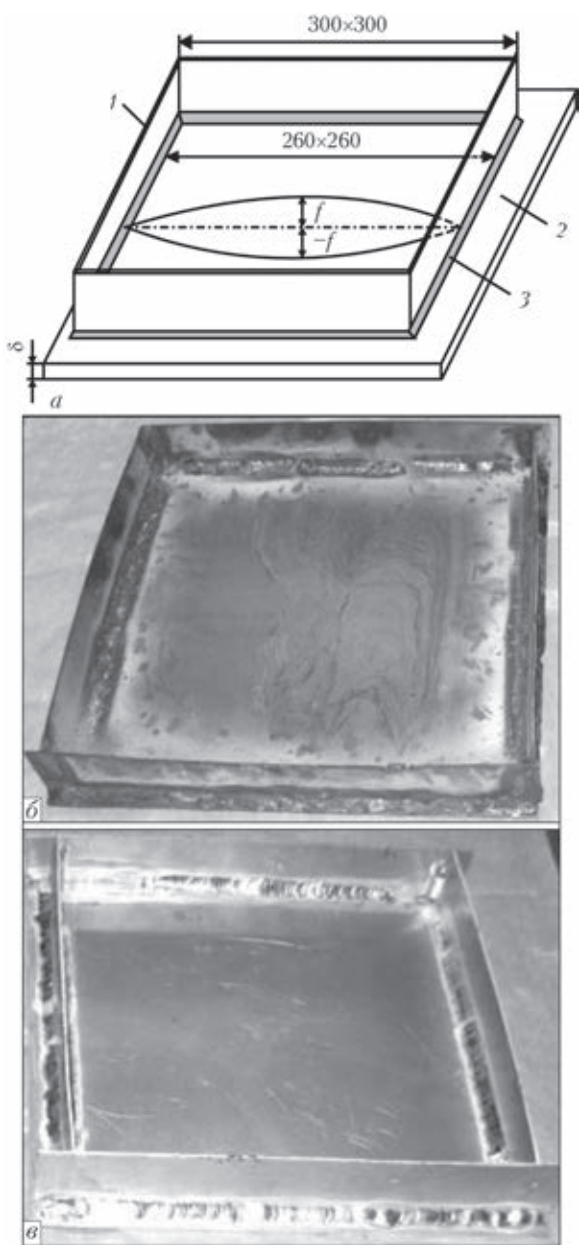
Схема образцов сварных соединений с деформацией типа бухтина (а) (1 — ребро; 2 — пластина; 3 — угловой шов) и внешний вид образцов соответственно из стали Ст3 (б) и сплава АМг6 (в)
